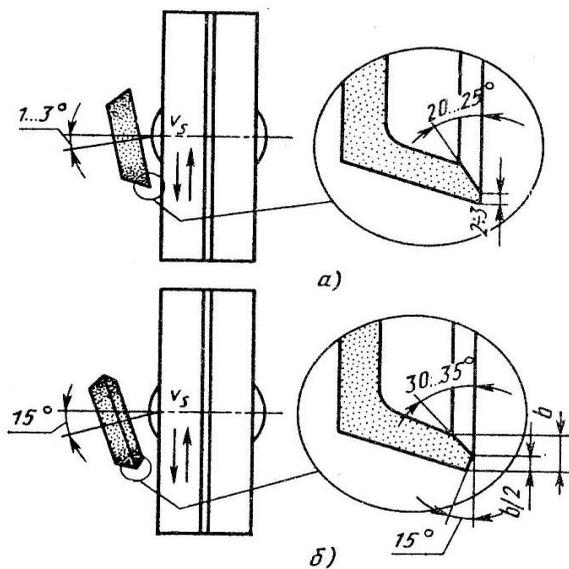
Форма рабочей поверхности шлифовального круга для заточки задних поверхностей развёрток: а) торцом; б) конусом
